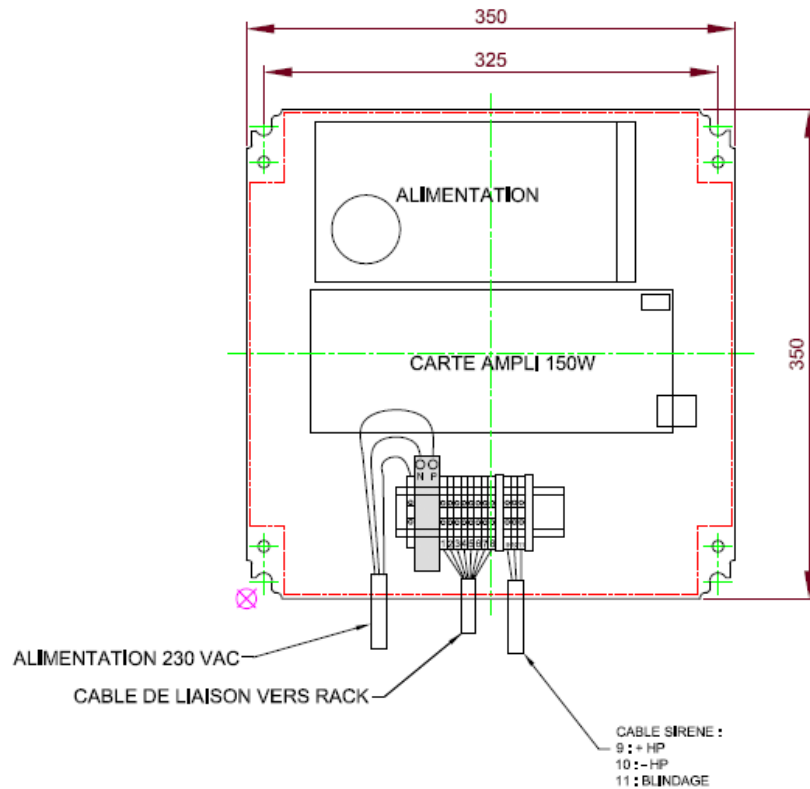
Plaque de fond du coffret d'extension de rack Tunneligée
